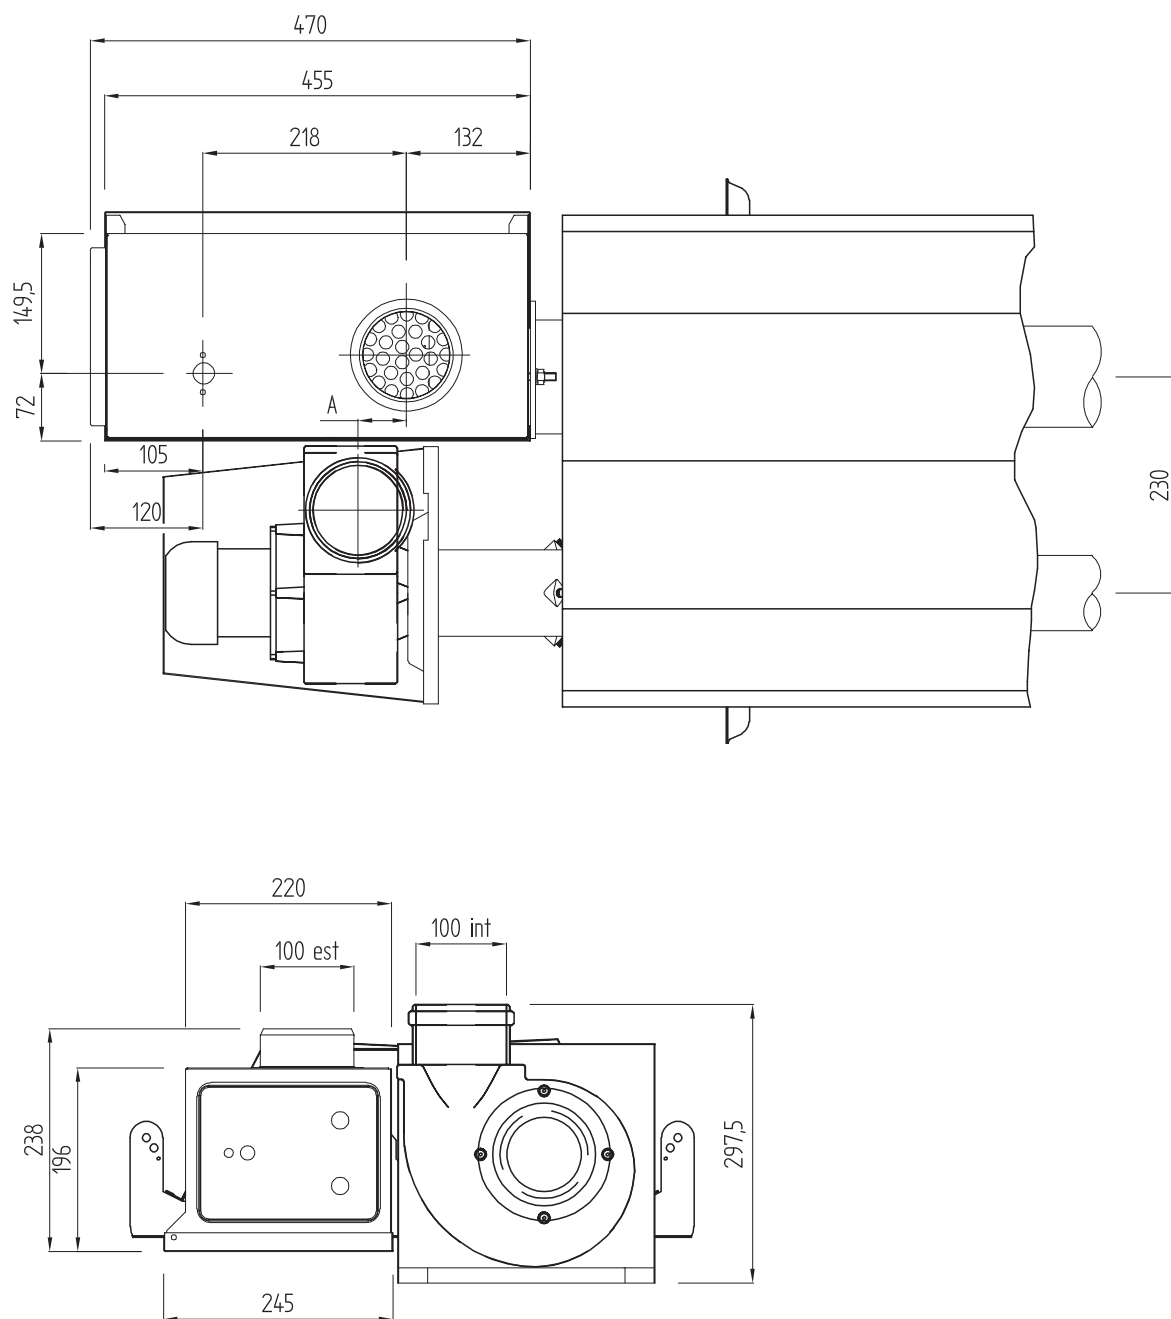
Размеры горелки BAF и вытяжного вентилятора
